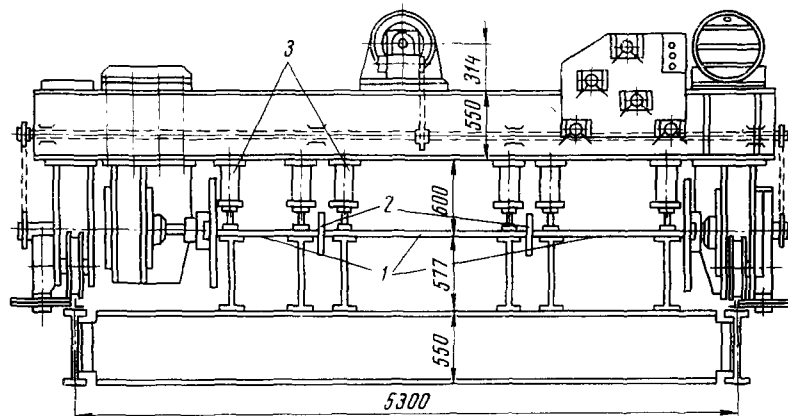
Самоходный портал для сборки балок больших размеров
